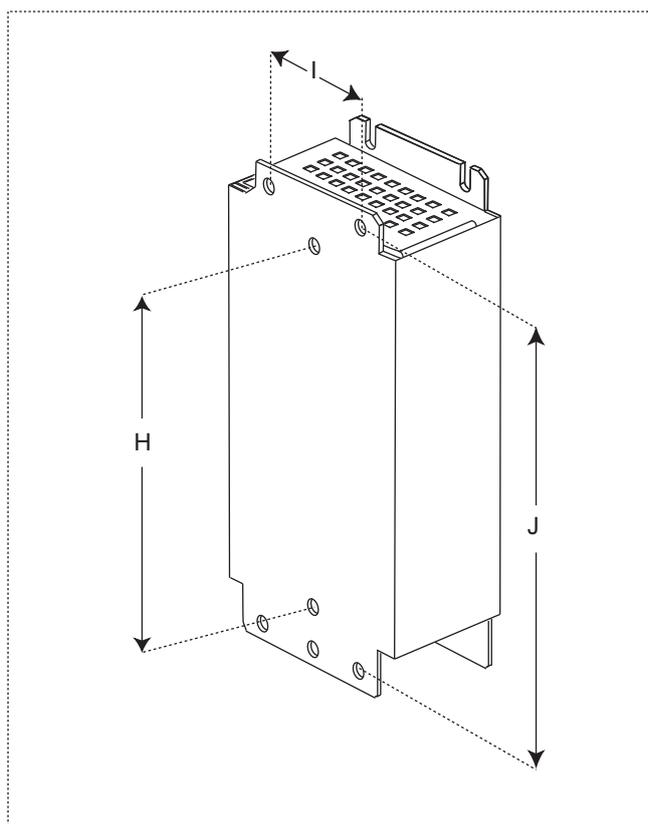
Quote di montaggio bobina motore, grandezza costruttiva FSA
